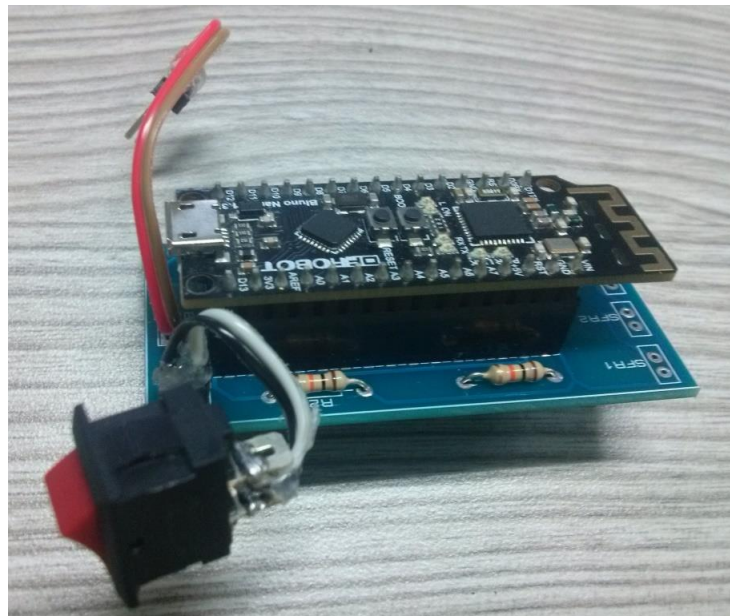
Tarjeta PCB con los componentes soldados.
